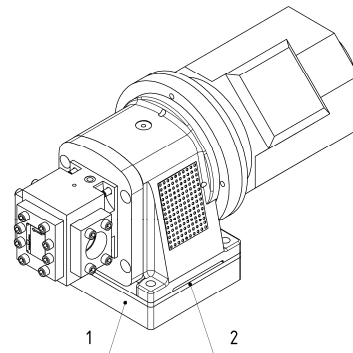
Шестеренчатый насос на фундаменте; 1 = Фундамент или стальная рама; 2 = Демпфирующий элемент
